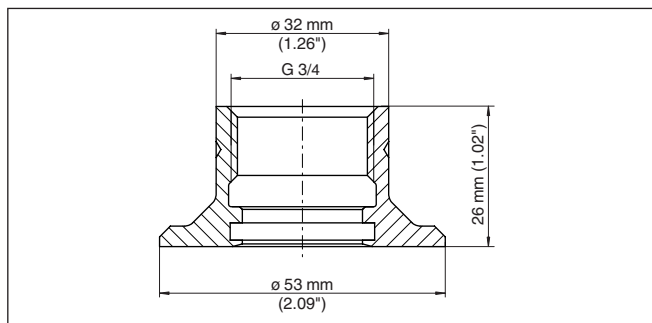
Dimensiones racor para soldar G $\frac{3}{4}$ (DIN 3852-A, ISO 228-1)
